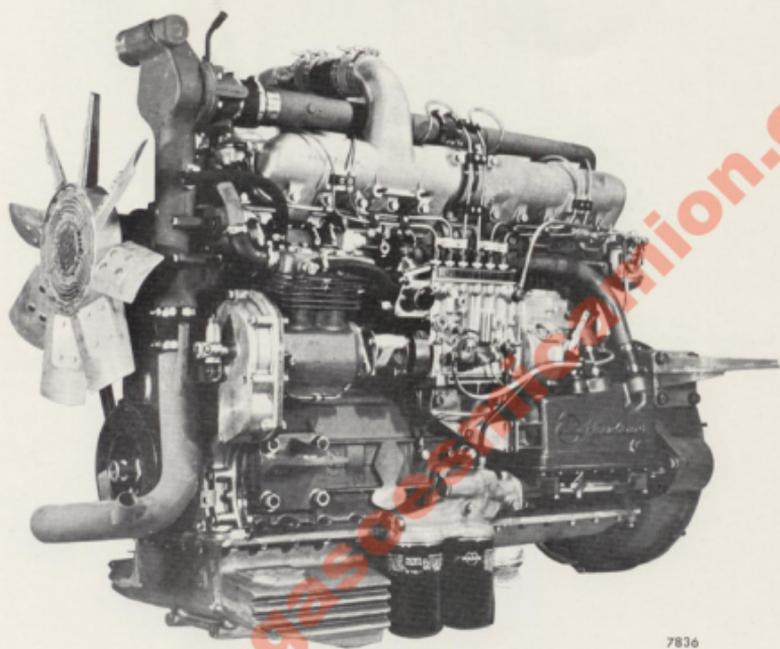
Motor 9156, lado izquierda (Montaje DESDE)
